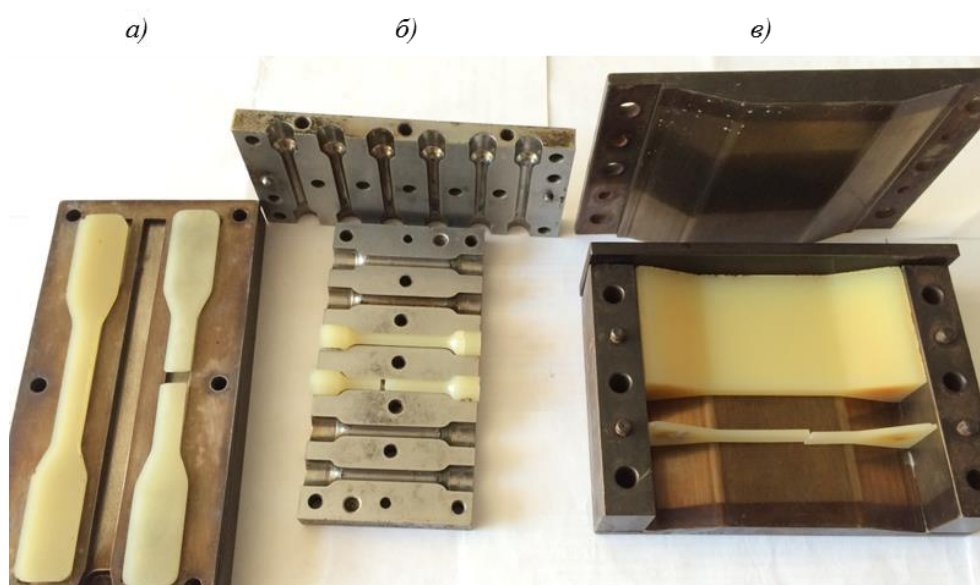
Вид оснасток для изготовления образцов по способам 1 (а), 2 (б) и 3 (в)
